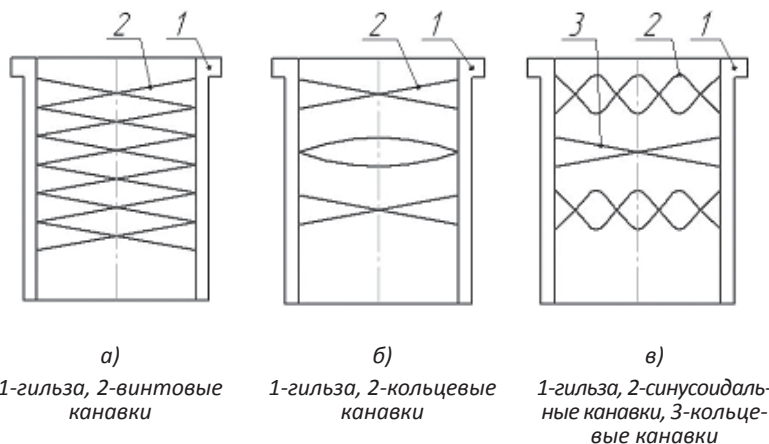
Схема металлизации гильзы цилиндра: а) гильза с винтовыми канавками; б) гильза с кольцевыми канавками; в) гильза с синусоидальными и кольцевыми канавками
